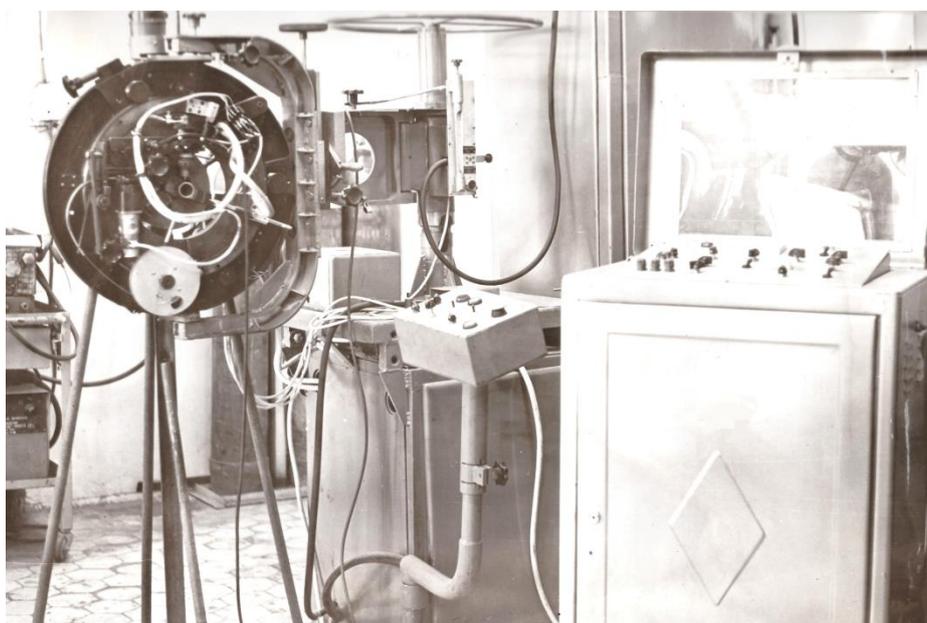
Установка для сварки неповоротных стыков трубопроводов
